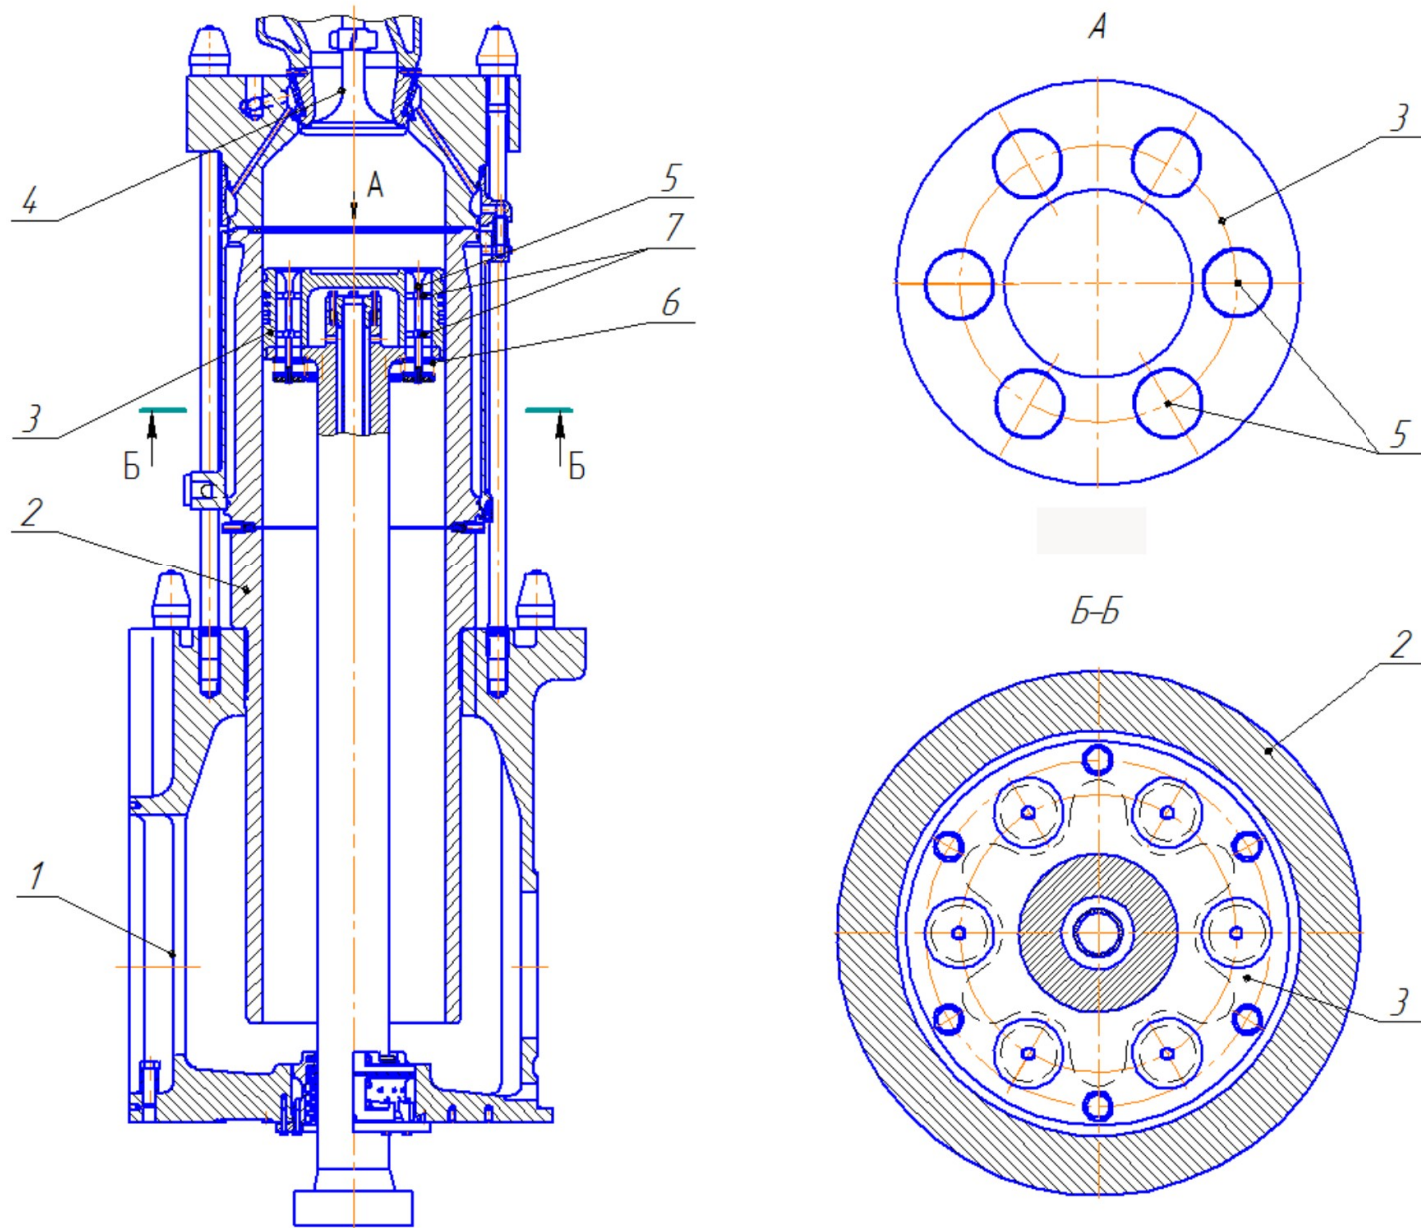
Загальний вигляд прямоточно-клапанної системи газообміну двотактного дизеля: 1 - ресивер продувного повітря; 2 - циліндрова втулка; 3 – поршень; 4 - випускний клапан; 5 - продувні клапани; 6 – пружина; 7 - крилатки
